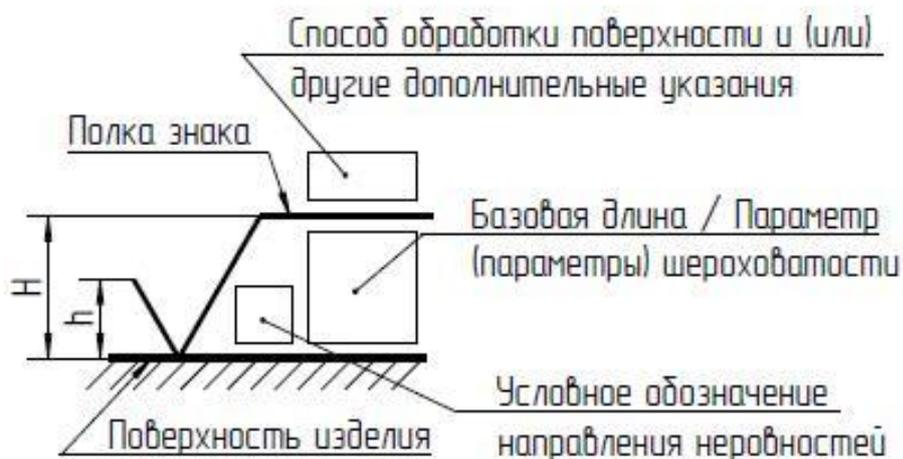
Обозначение шероховатости поверхности на чертеже
